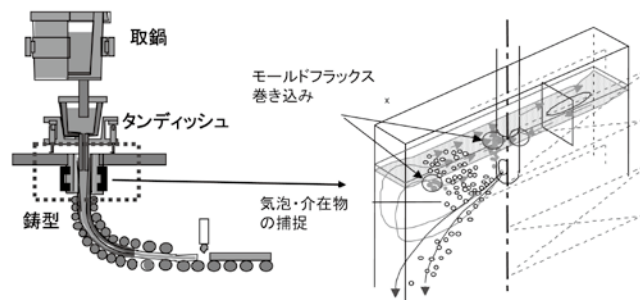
連铸 casting 型内溶鋼流動と鑄片欠陥発生機構の模式図
